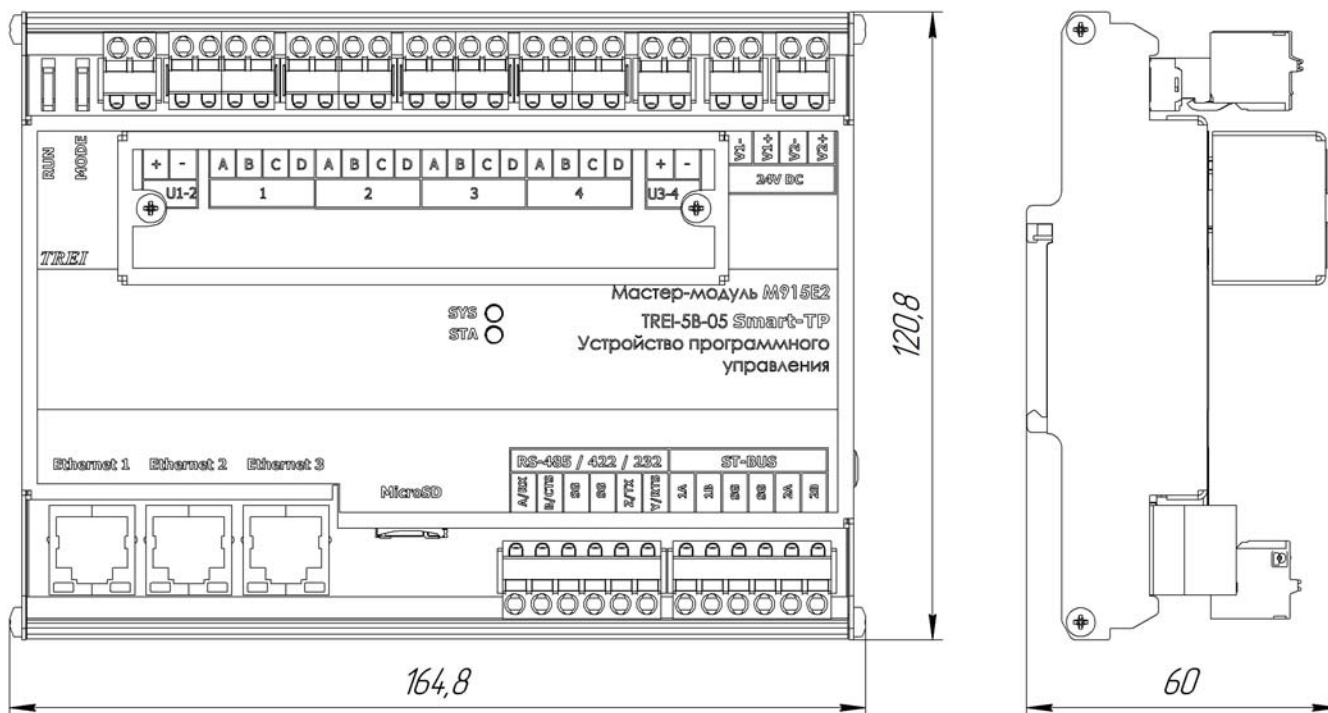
Чертеж общего вида M915E2 с указанием габаритных и присоединительных размеров
